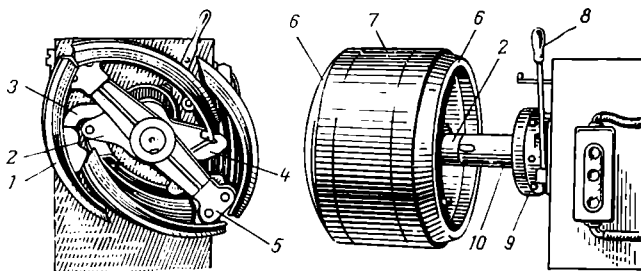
Жесткий металлический полуплоский барабан станка для сборки покрышек: 1 — сектор барабана; 2 — рычажная муфта; 3, 4 — рычаги; 5 — крестовина; 6 — плечики; 7 — корона; 8 — рукоятка тормоза; 9 — тормоз; 10 — полый вал.
